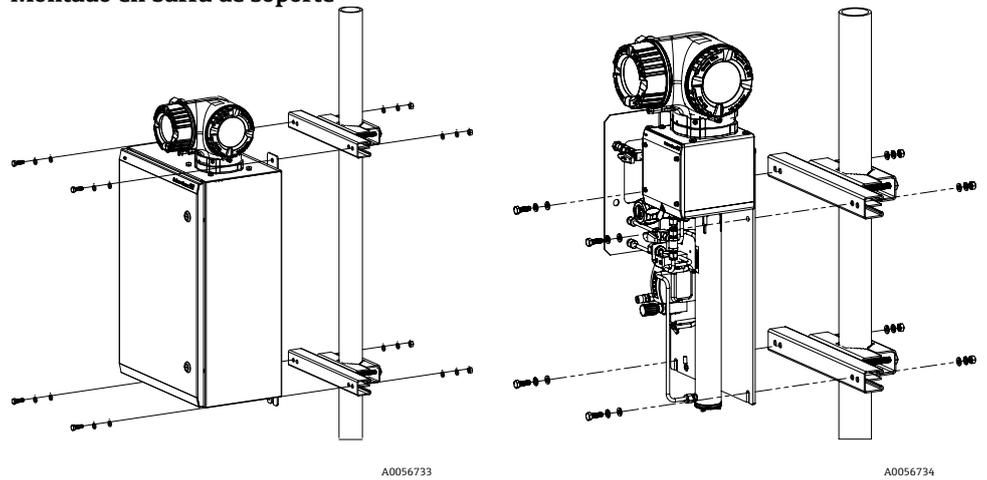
Montaje en barra de soporte del analizador de gas TDLAS J22 con envolvente (izquierda) y en un panel (derecha)
